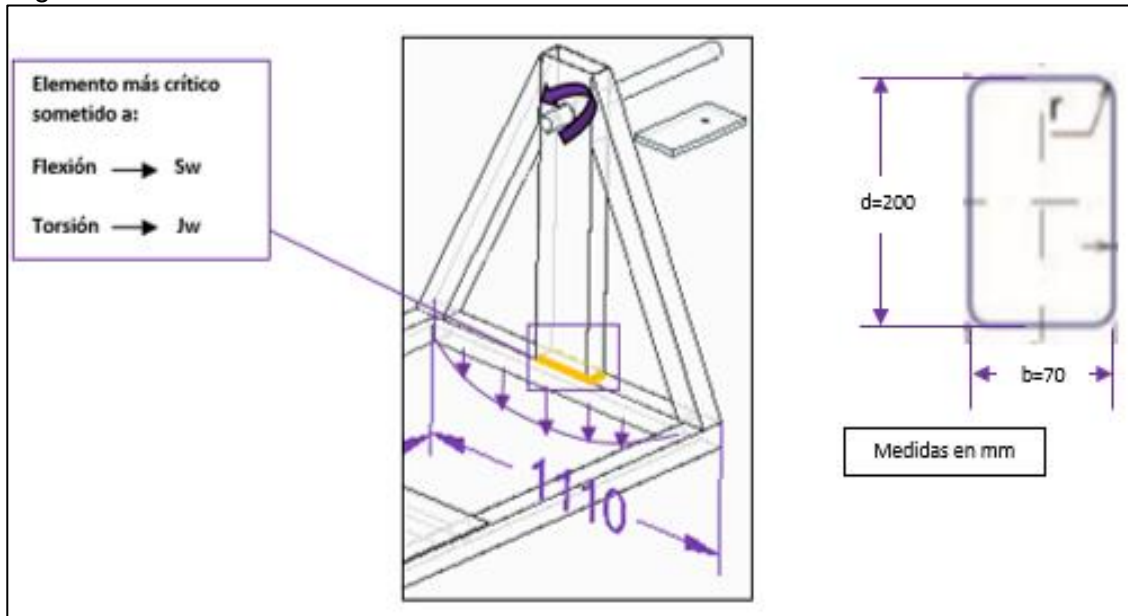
Factores geométricos para el análisis de soldaduras
